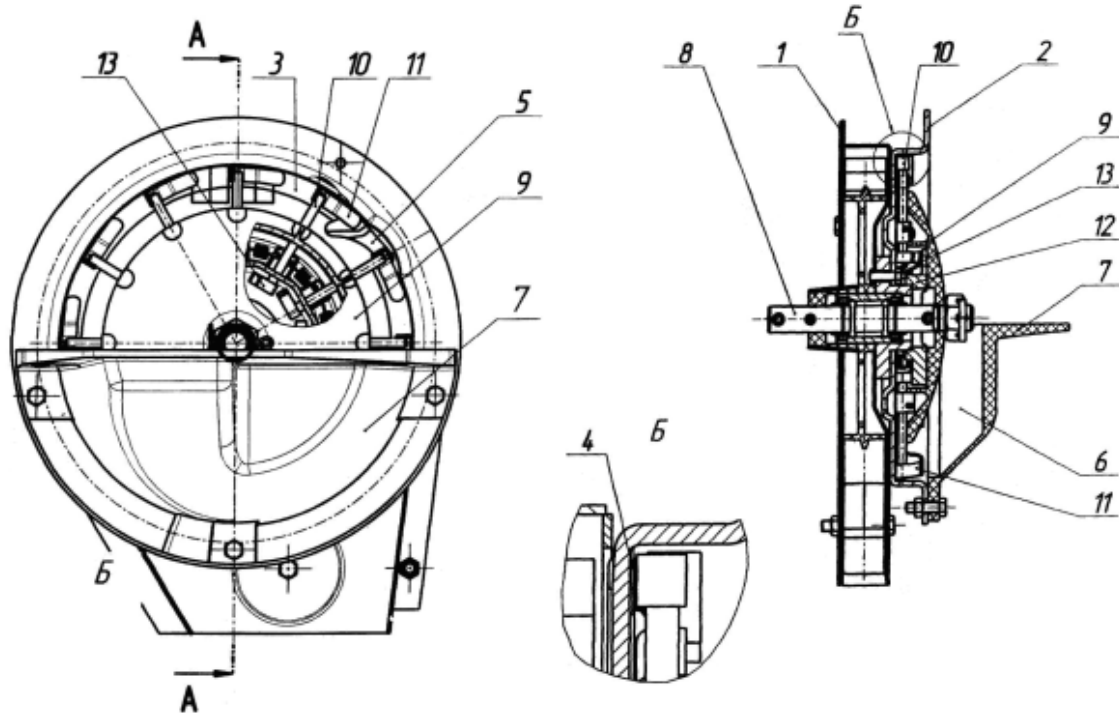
Схема висівного апарату: 1 - корпус; 2 - висівний диск; 3 - напрямна доріжка; 4 - полімерних; 5 – викидне вікно; 6 - камери для насіння; 7 - кришка корпусу; 8 - привідна вісь; 9 - обтічник; 10 - шток; 11 – палець; 12 – корпус кулачка; 13 - хвостовик.
